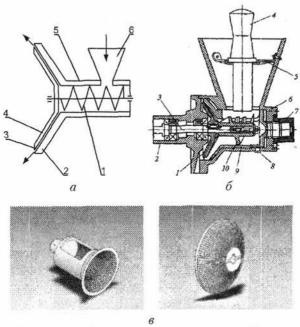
Размолочный механизм с конусными рабочими органами: a — схема механизма: 1 — подающий шнек; 2 — неподвижный жернов; 3 — зазор между жерновами; 4 — подвижный жернов; 5 — корпус; 6 — бункер загрузочный;  $\delta$  — общий вид: 1 — диск терочный (вращающийся жернов); 2 — хвостовик; 3 — вал; 4 — толкатель; 5 — предохранительная решетка; 6 — корпус; 7 — гайка; 8 — винт; 9 — барабан; 10 — шнек;  $\theta$  — жернова
